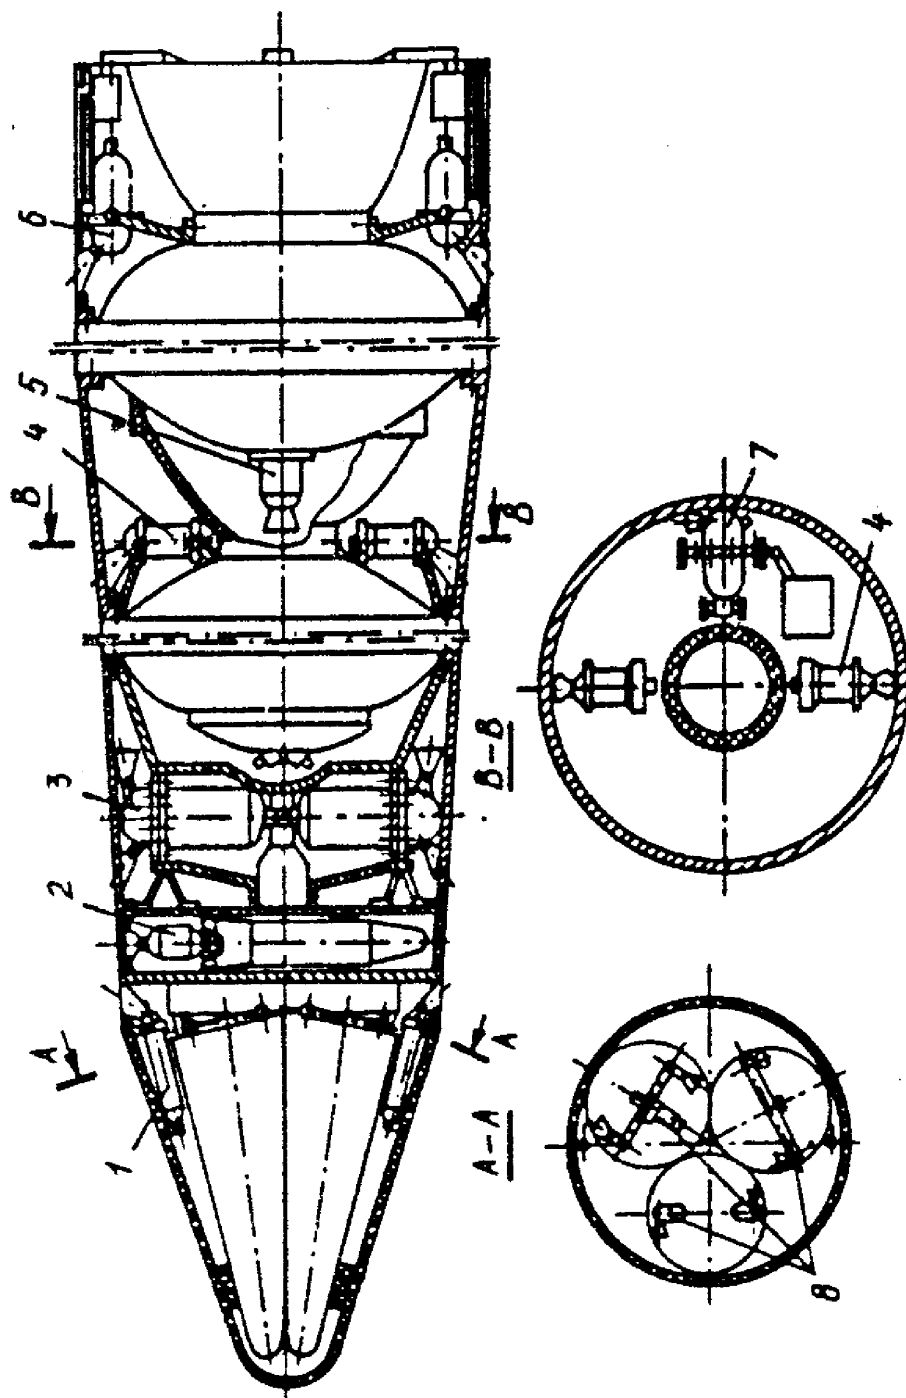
Схема размещения ДСН на гипотетической многоступенчатой твердотопливной ракете:
